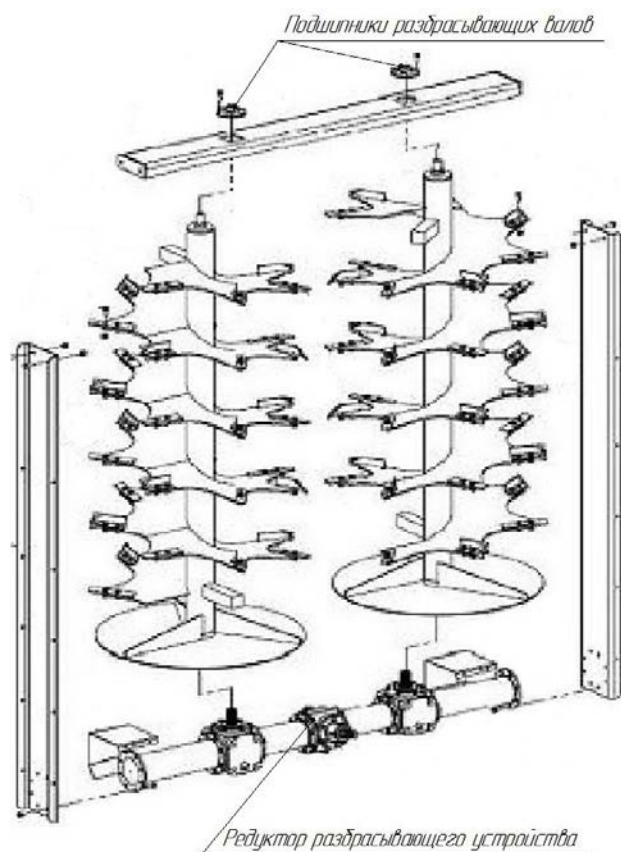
Смазка редуктора и подшипников разбрасывающих валов
